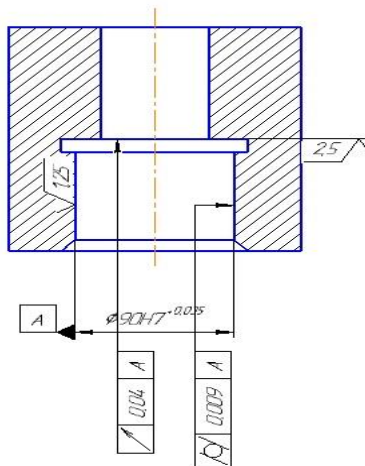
Изображения поля допуска подшипника для отверстия
